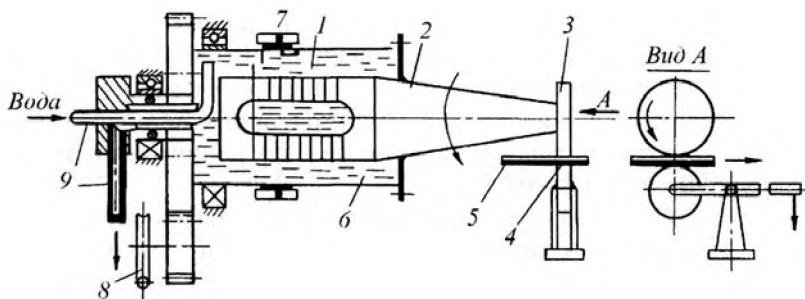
Схема установки для роликовой сварки ультразвуком: 1 – магнитострикционный преобразователь; 2 – волновод; 3 – сваривающий ролик; 4 – прижимной ролик; 5 – изделие; 6 – кожух преобразователя; 7 – подвод тока от ультразвукового генератора; 8 – привод; 9 – подвод охлаждающей воды
